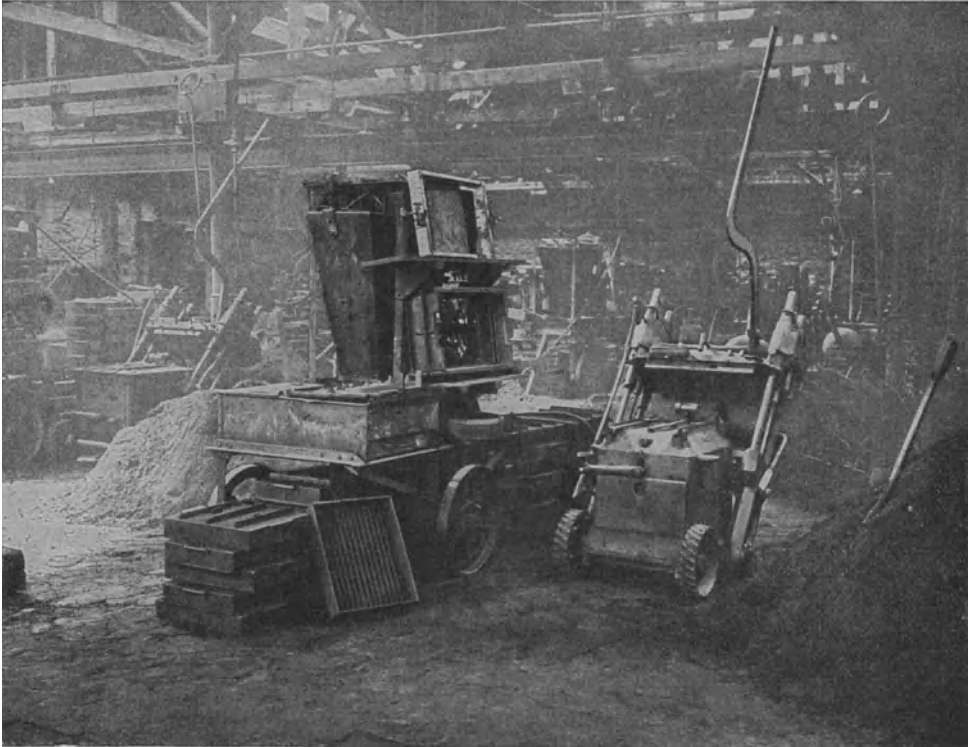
Vosssche Formmaschine mit Gerätewagen.
